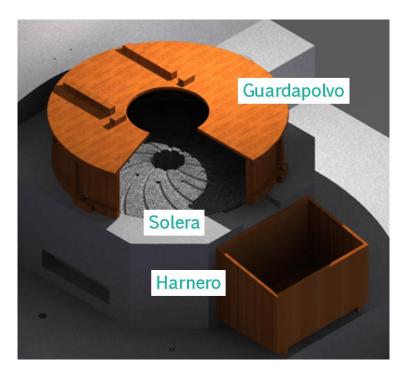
Vista general del conjunto solera, guardapolvo y harnero.
